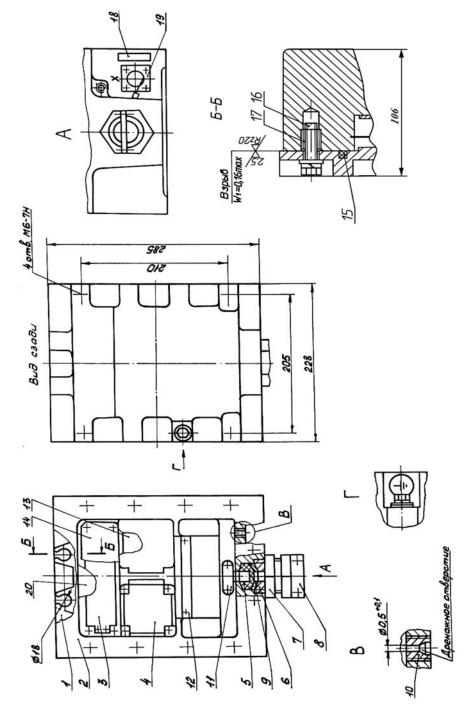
Преобразователь нормирующий. Внешний вид и габаритные размеры: 1,14,20- крышки; 2- корпус; 3- плата блока питания; 4- плата функционального блока; 5,6,17- втулки; 7- гайка; 8- планка; 9- шайба; 10- винт; 11- скоба; 12- колодка; 13- плата генератора; 15- кольцо; 16- болт; 18- табличка; 19- соединитель
